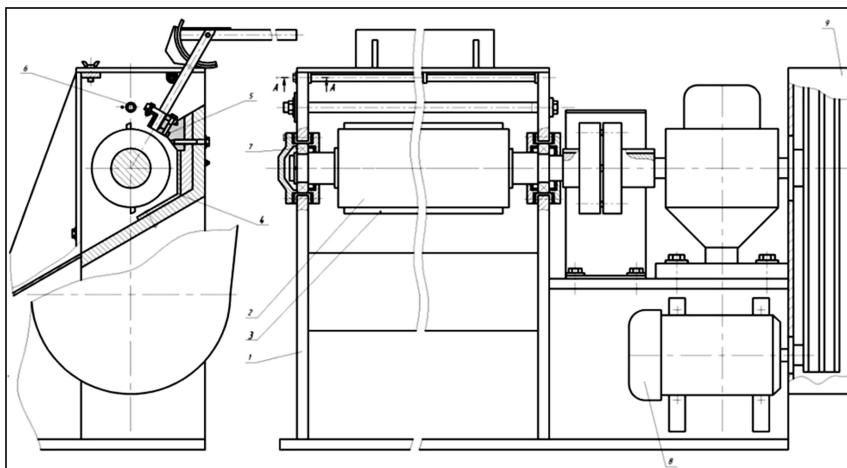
Подрібнювач порохів: 1 – станина; 2 – ротор; 3 – ножі; 4 – лоток; 5 – нерухомий ніж; 6 – колектор; 7 – обійми; 8 – двигун; 9 – кожух
